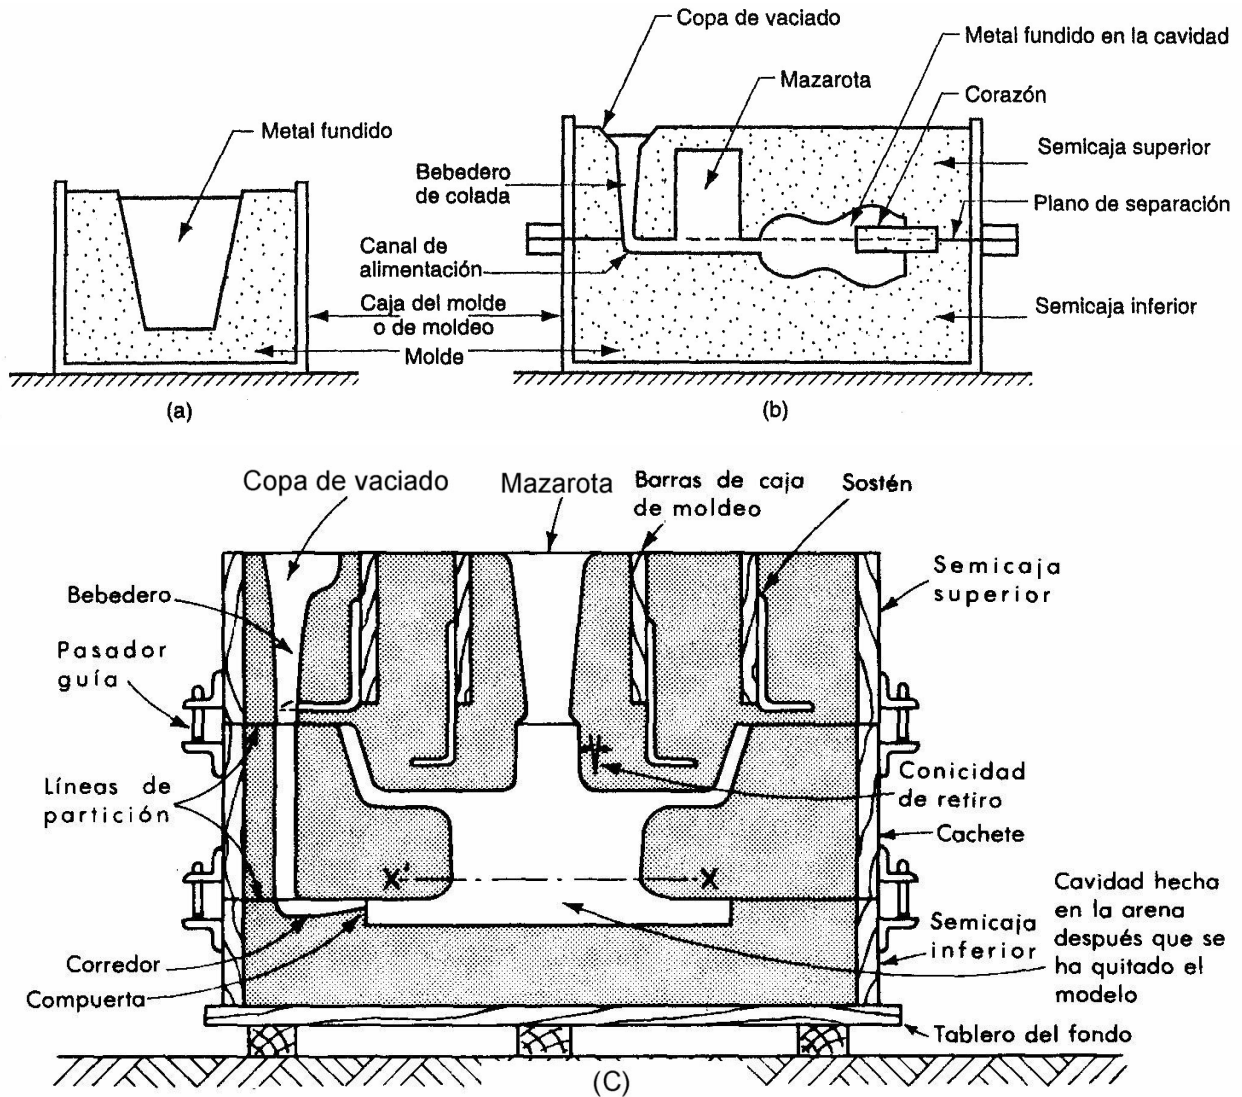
Dos formas de molde: (a) molde abierto, simplemente un recipiente con la forma de la parte de fundición; (b) molde cerrado, de forma más compleja que requiere un sistema de vaciado (vía de paso) conectado con la cavidad; y c) Sección transversal de un molde en tres partes
